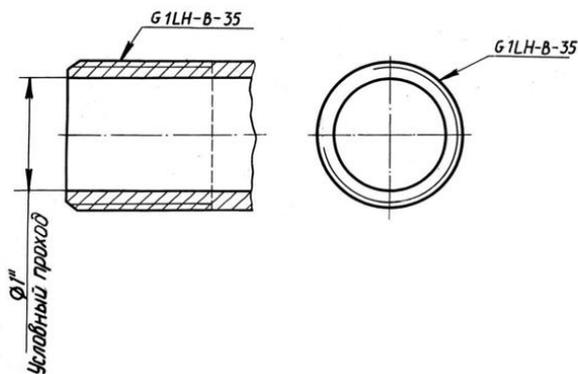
Обозначение наружной цилиндрической трубной резьбы
